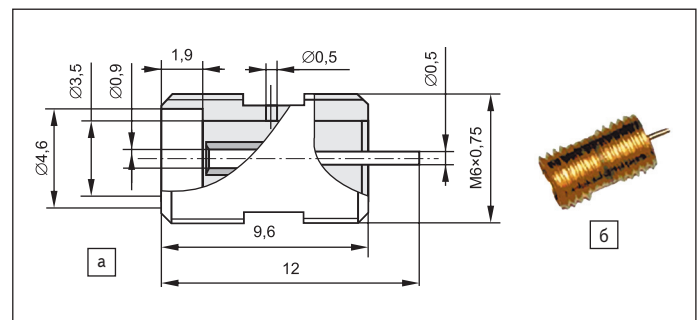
Соединитель TC2.236.072-01: а) конструкция; б) внешний вид
